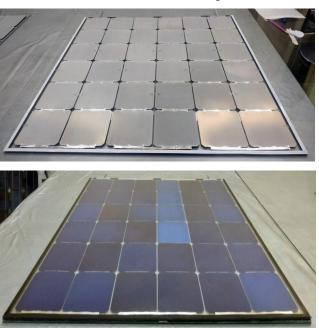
Сборка фотоэлектрического модуля и подготовка пакета для заливки
